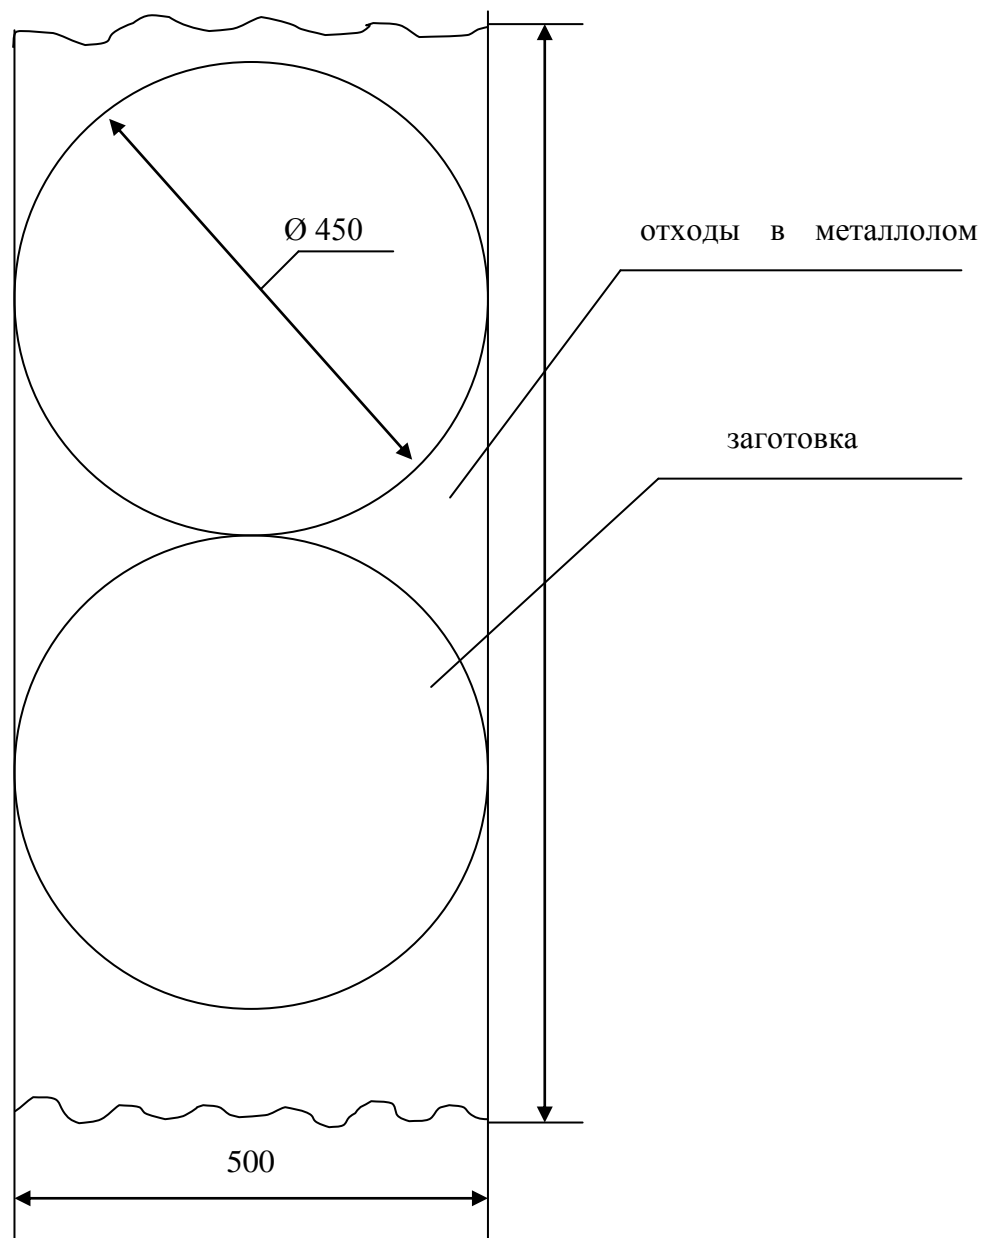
План раскроя стабильного листа для изготовления заготовок верхнего и нижнего корпусов пылесоса "Вихрь – 8А"
